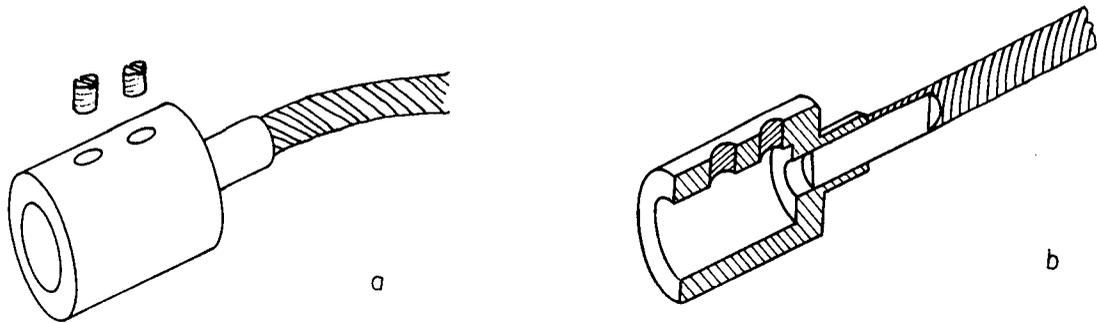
Flange de conexão veio flexível/eixo do motor: a) vista em perspectiva; b) perspectiva em corte.
